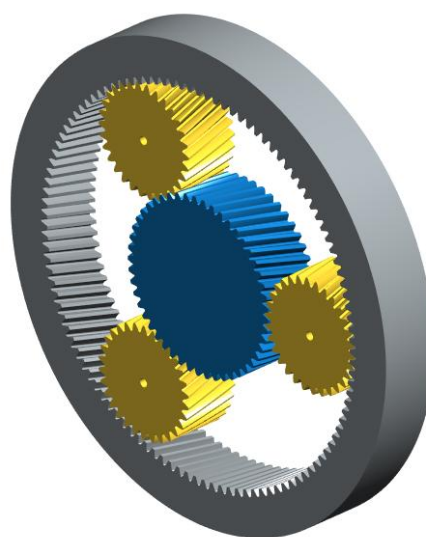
3º estágio; Engrenagens planetárias a amarelo; Engrenagem solar a Azul; Engrenagem anelar a cinzento
